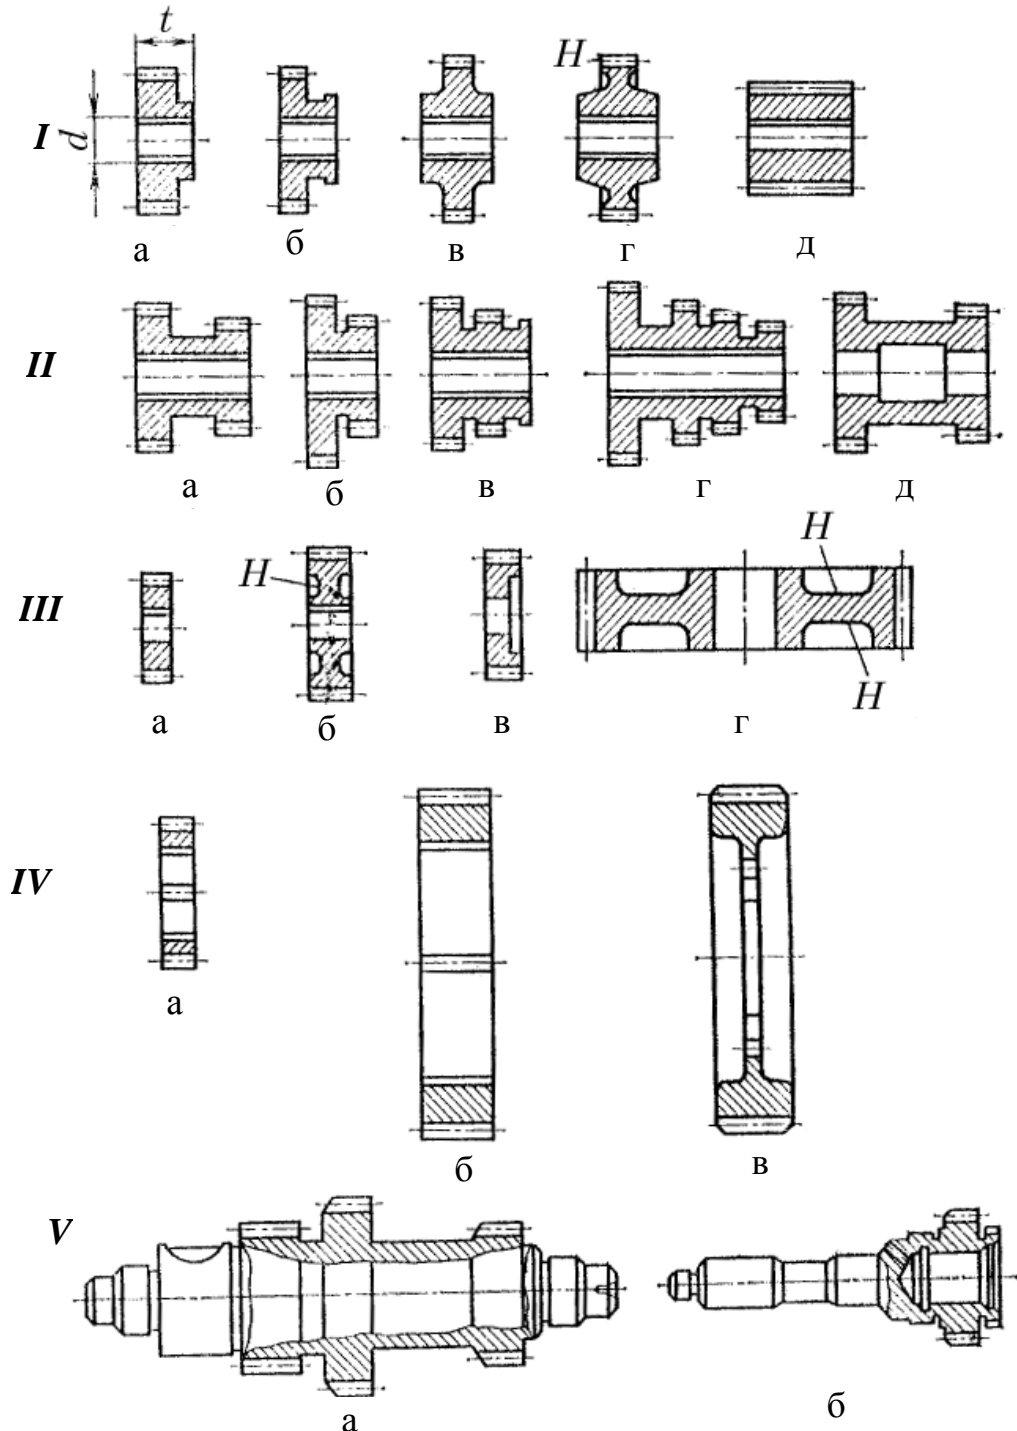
Конструктивні різновиди циліндричних зубчастих коліс.
